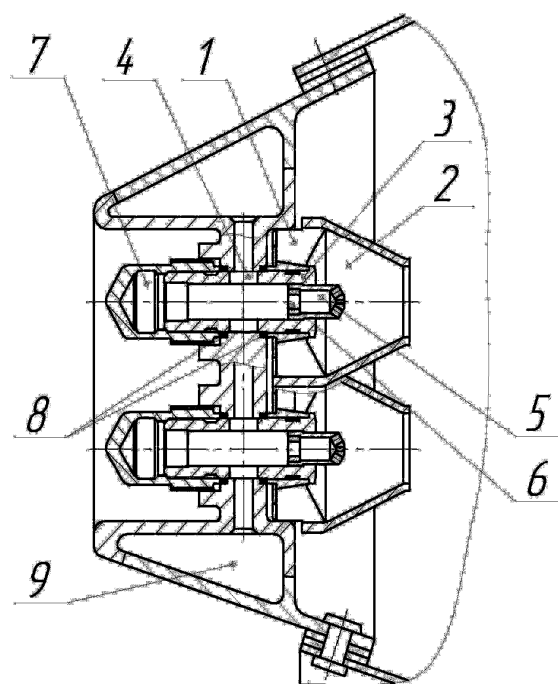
Конструкция форсунки кольцевой камеры сгорания двигателя НК-16-18СТ
